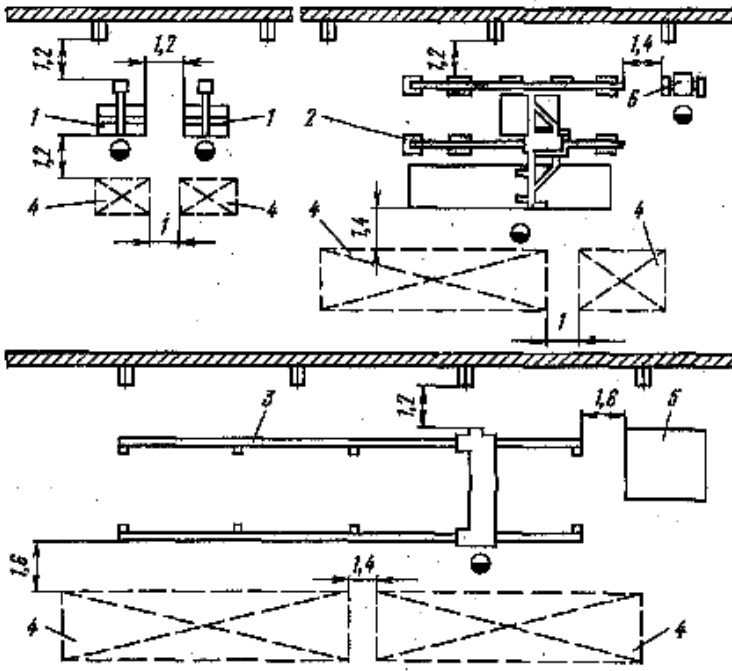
Схеми розташування машин для кисневого різання сталі:
